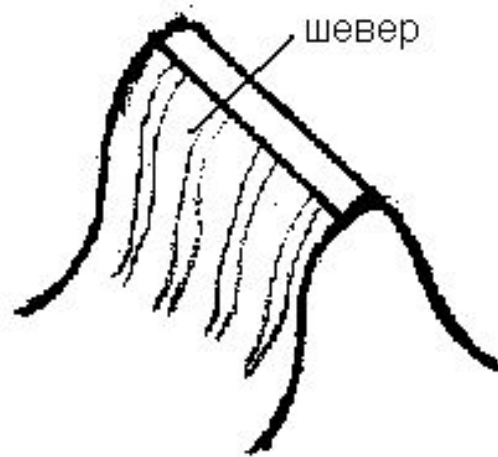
Режущие канавки на поверхности зубьев шевера
